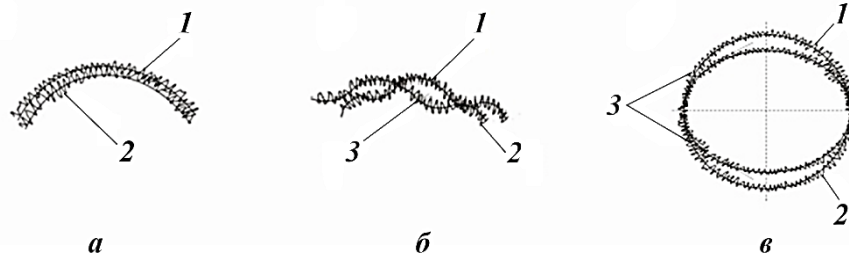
Схемы контактирования в неподвижных соединениях при наличии шероховатости (а), шероховатости и волнистости (б), шероховатости и овальности (в): 1 – охватывающая поверхность (штуцер); 2 – охватываемая поверхность (ниппель); 3 – поры, формирующиеся в неподвижном контакте
